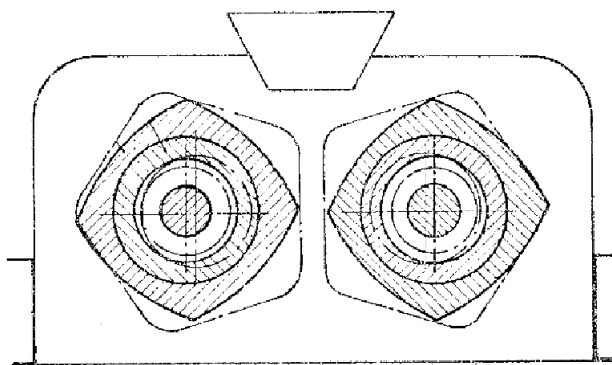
Схема валкой дробилки (авторское свидетельство SU № 1726017) [2]
